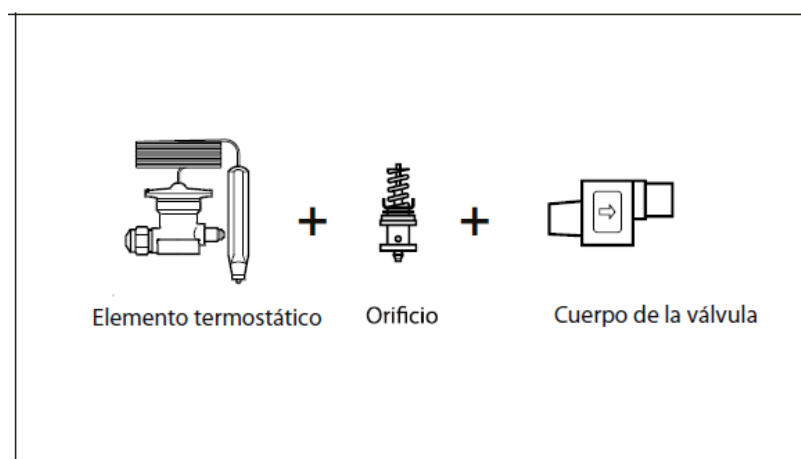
Parts de la vàlvula termostàtica a escollir
